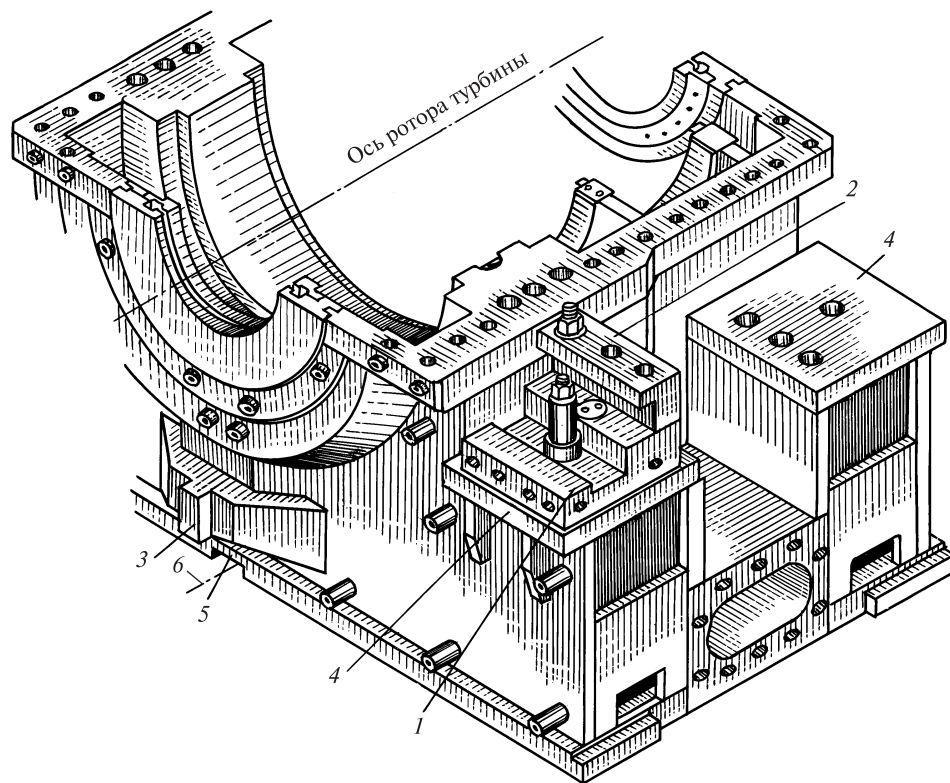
Общий вид нижней половины корпуса среднего подшипника турбины Т-250/300-23,5 ТМЗ
